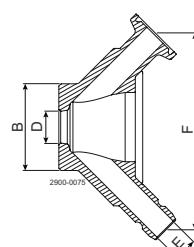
Cuerpo de la válvula: Depósito (para soldar)
